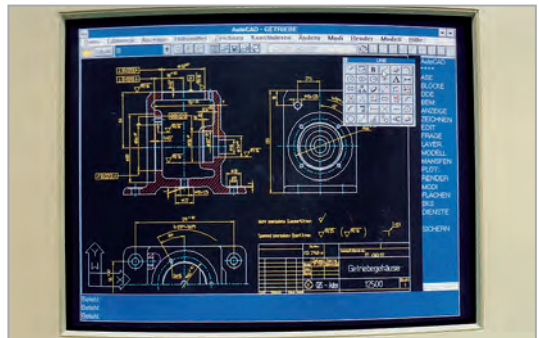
CAD als Hilfsmittel zum Zeichnen (2D-CAD), um 1970
